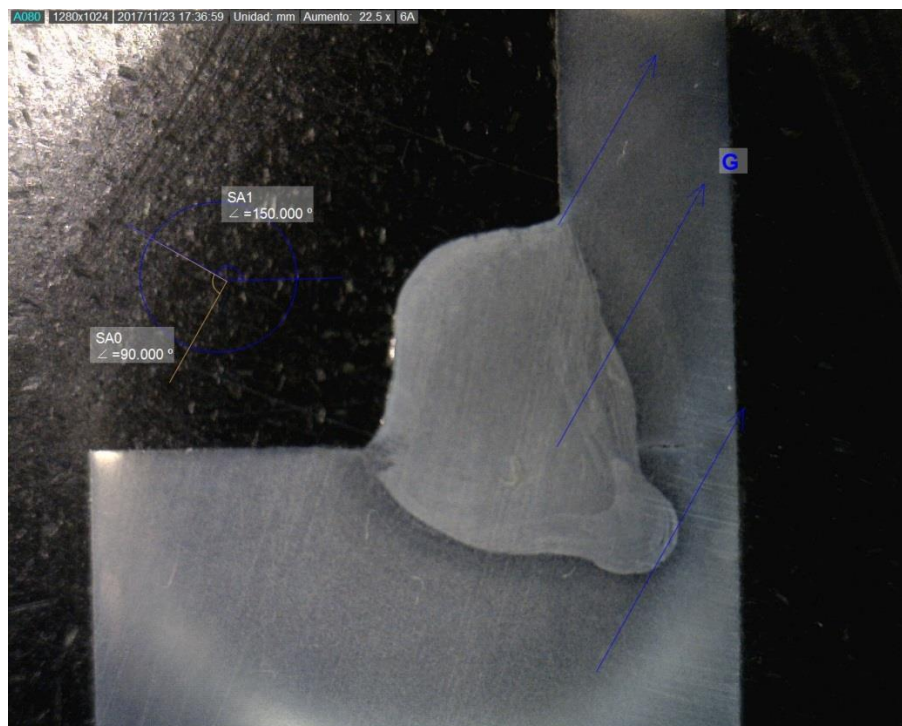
12 Perfil obtenido en cupón de soldadura 6B.
